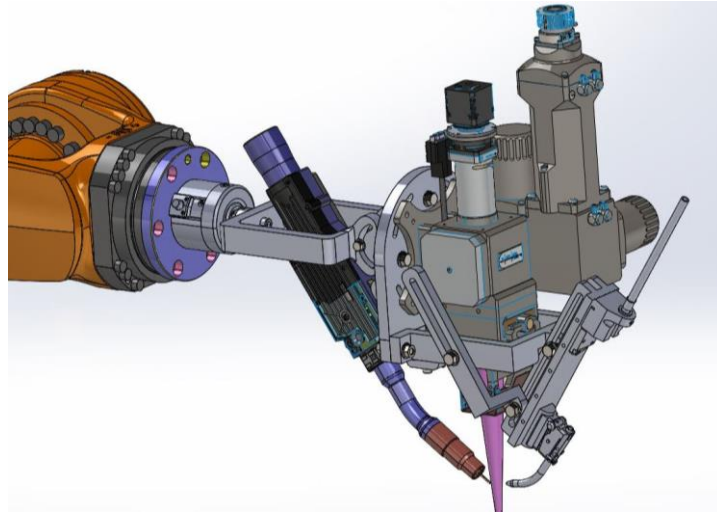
11 Sistema de herramientas de soldadura montadas en el cabezal (1)
